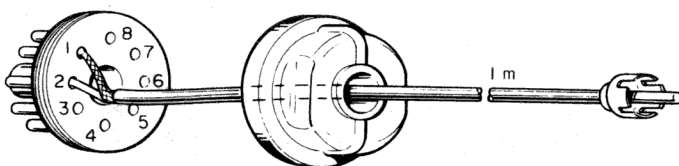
Coax-Anschlußkabel für den Panorama-Adapter
